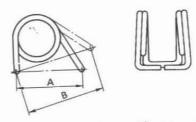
Esquema de comprobación del muelle de la palanca: A - dimensión en estado libre; B - dimensión bajo
